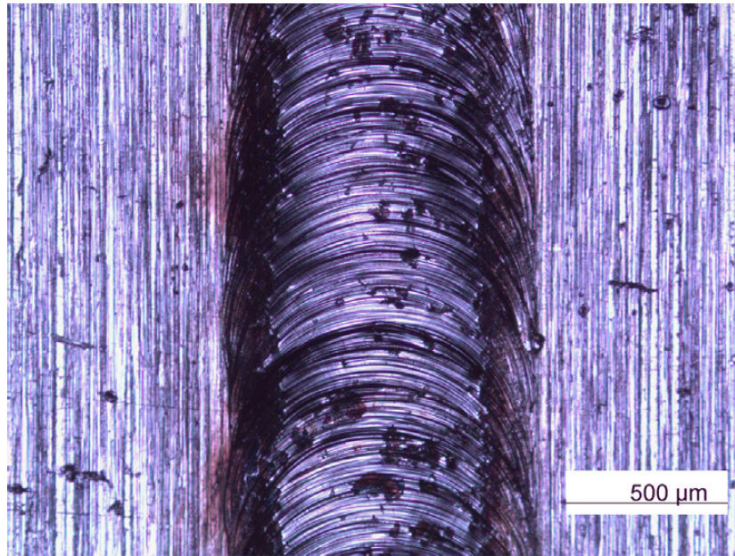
Schweißbad an der Oberseite einer schweißgelöteten Aluminium-Kupfer Verbindung [30]
